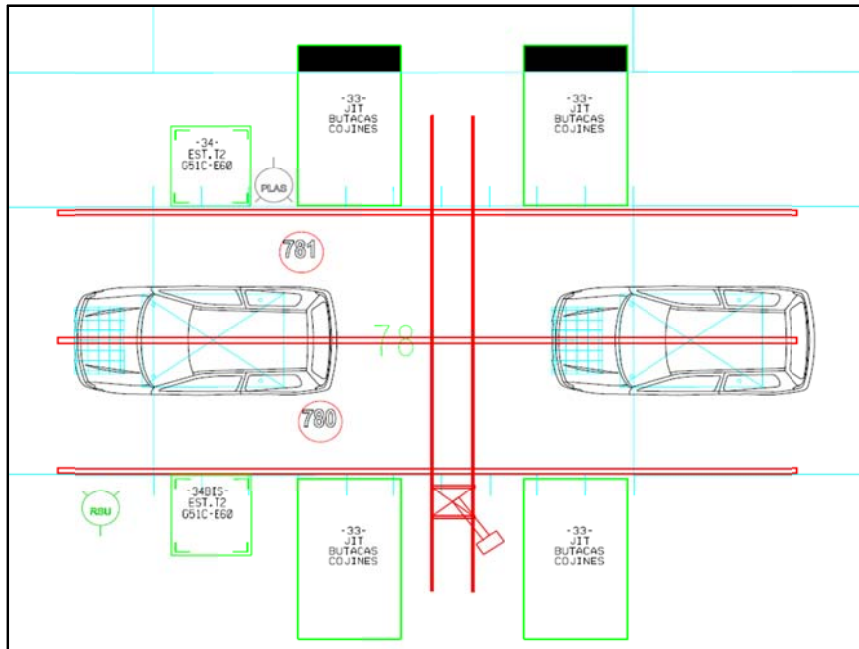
Layout manipulador montaje de butacas (opción 1 final)
